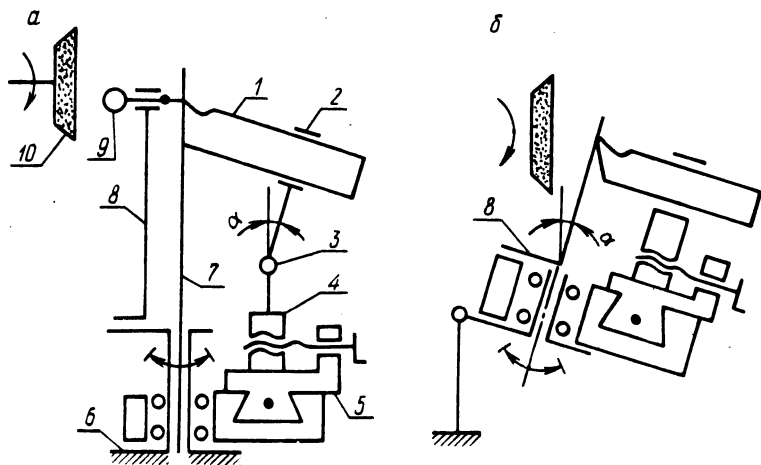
Принципиальные схемы приспособлений для заточки радиуса при вершине реза.
